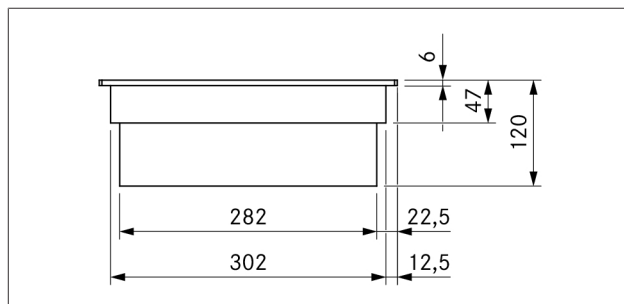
Dimensões do aparelho CKIW, vista frontal
